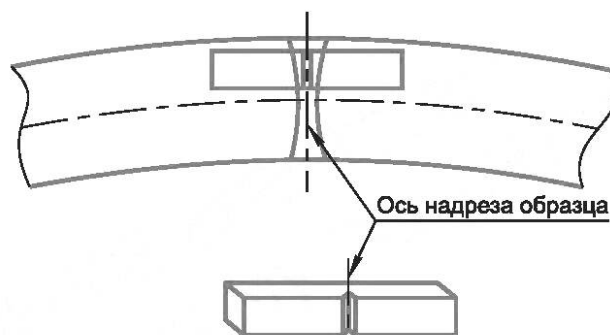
Ориентация надреза на образцах для испытаний на ударный изгиб
